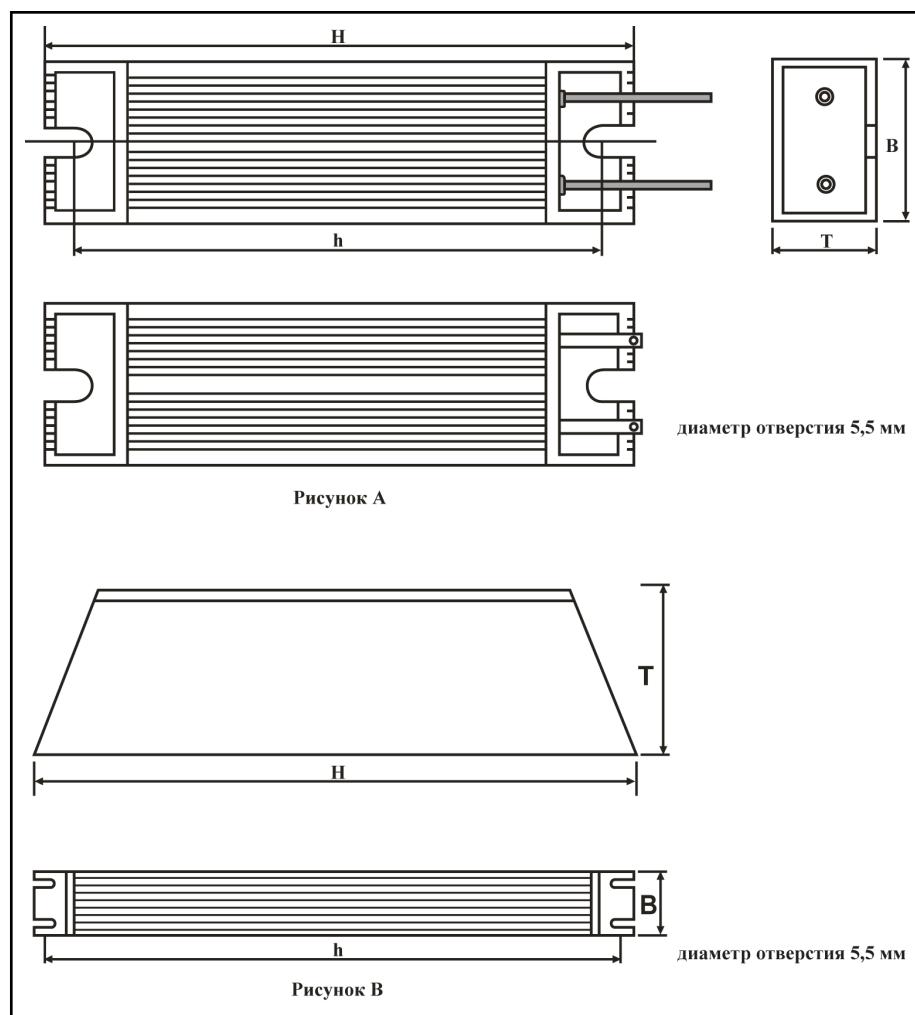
Тормозной резистор в алюминиевом корпусе
